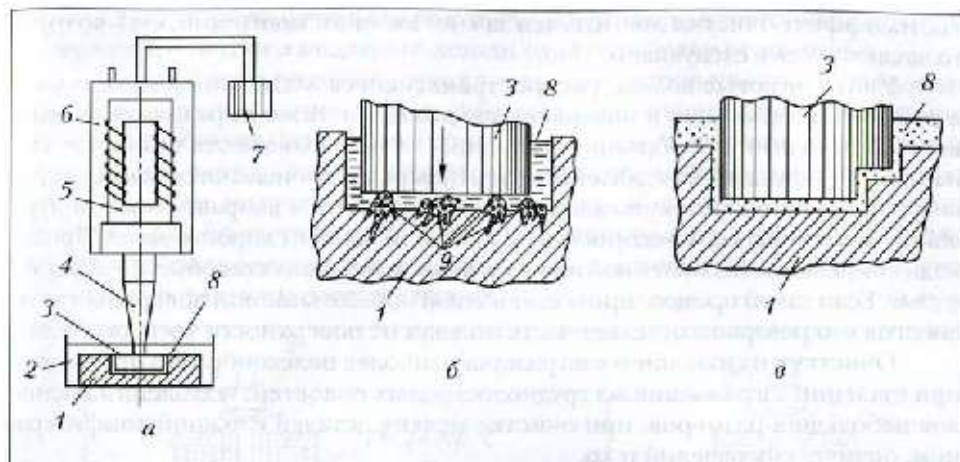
Ультразвуковая размерная обработка: а — принципиальная схема; б — схема съема материала при ультразвуковом прошивании; в — схема воспроизведения профиля инструмента в заготовке: 1 — заготовка; 2 — ванна; 3 — инструмент; 4 — волновод-концентратор (трансформатор амплитуды); 5 — преобразователь; 6 — корпус преобразователя; 7 — генератор тока ультразвуковой частоты; 8 — зазор, заполненный суспензией абразива; 9 — частички абразива (зерна)
